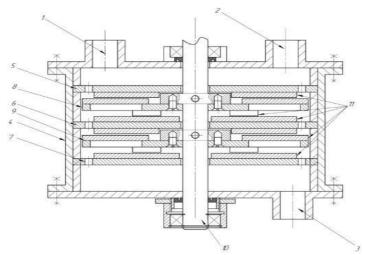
Двухступенчатый роторный измельчающий смеситель
